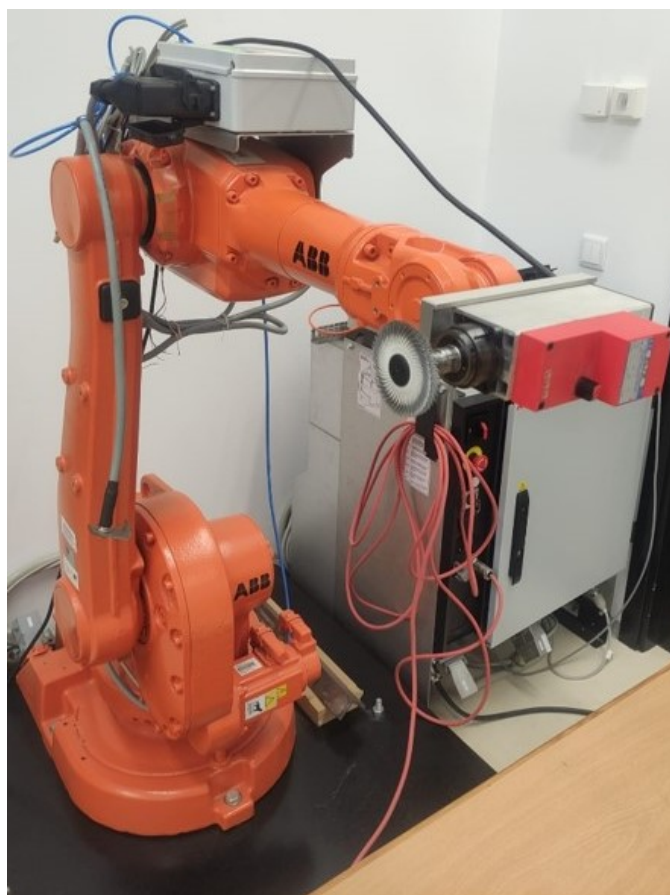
Robô ABB IRB1600, com o *spindle* Elte TMPE1 6.5/2 acoplado
